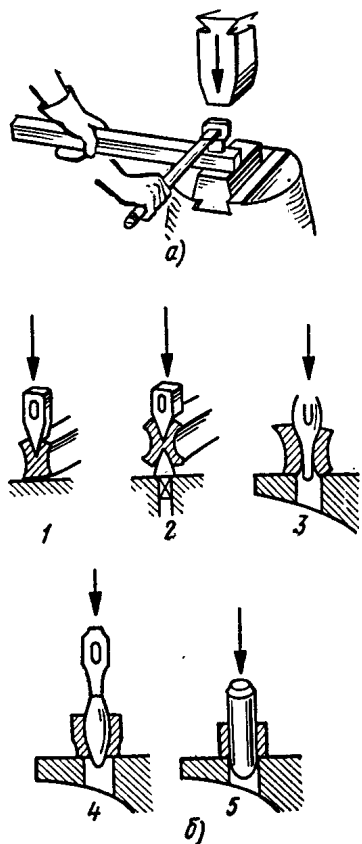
Схема пробивки и отделки отверстий у заготовок с недостаточно устойчивой опорой:
